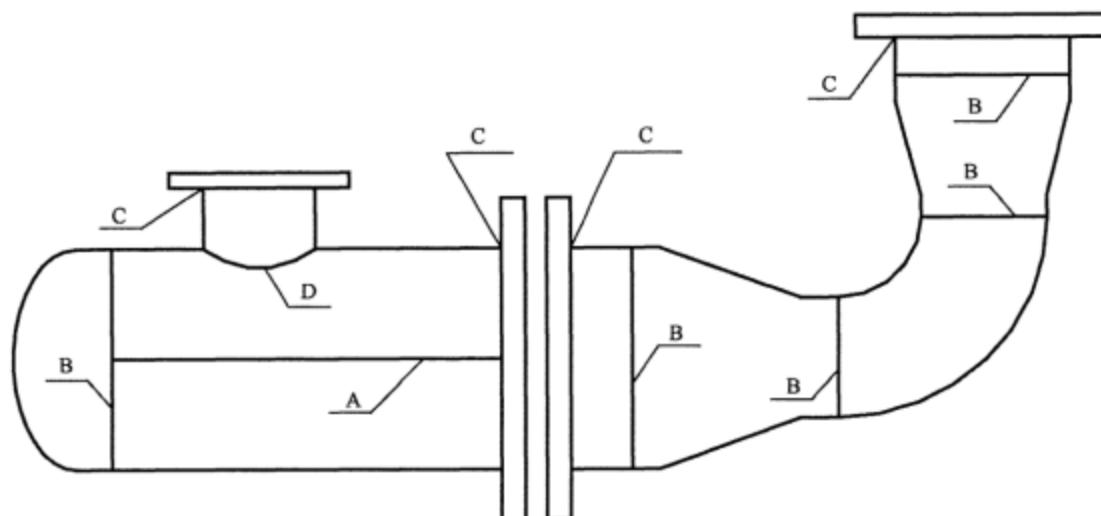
直埋式地下燃气调压装置管道承压部件的焊接接头分类
